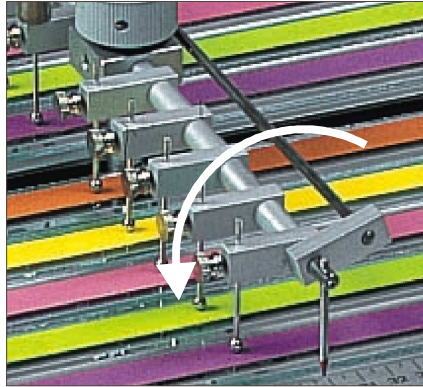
Schwenken Sie die Werkzeuge nach unten
